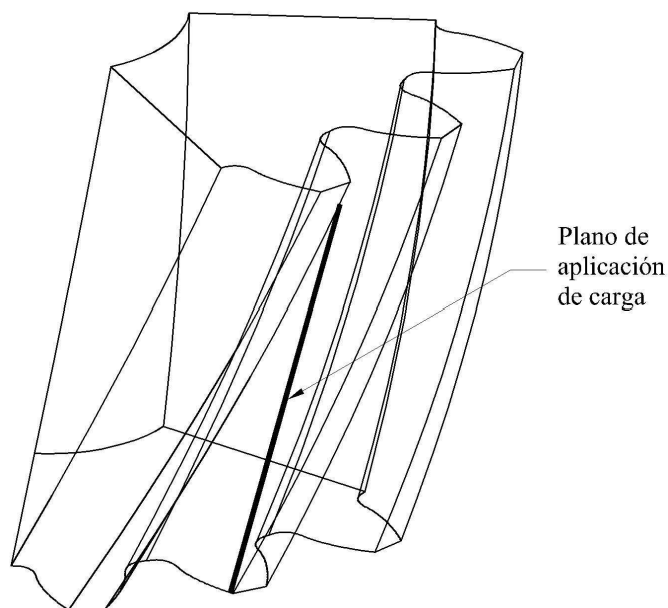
Modelo sólido de piñón con el plano de aplicación de carga
